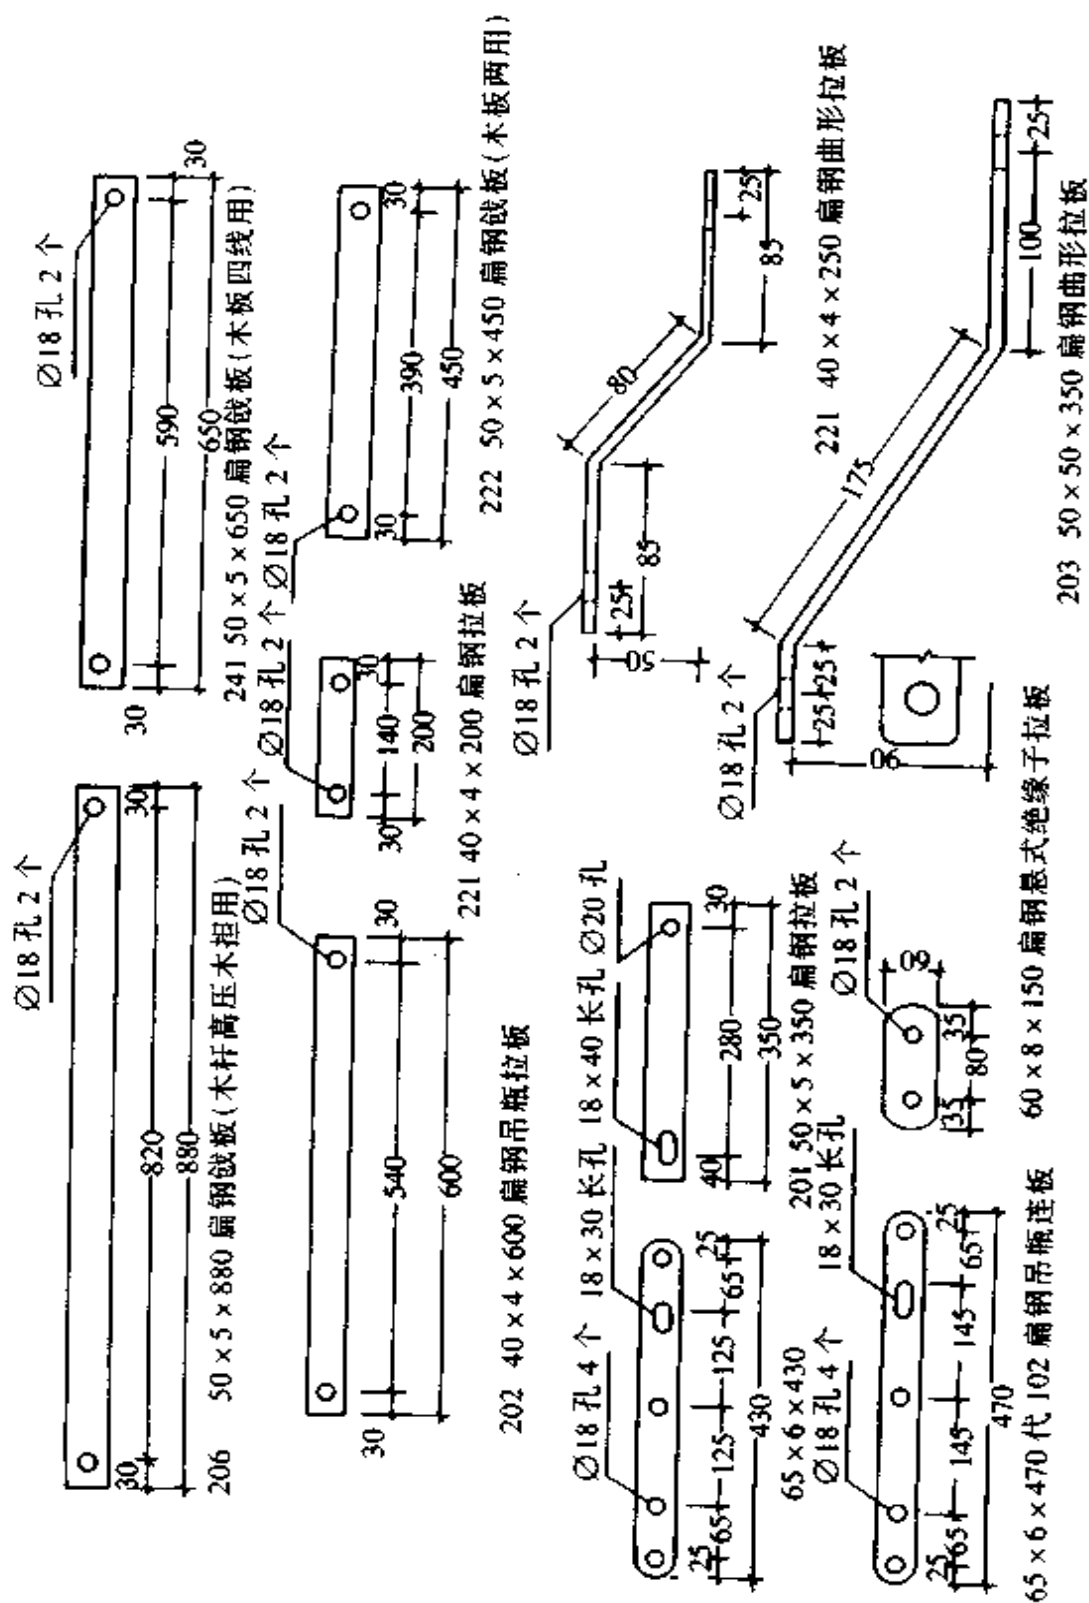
钢筋混凝土电杆附件加工图(二)
